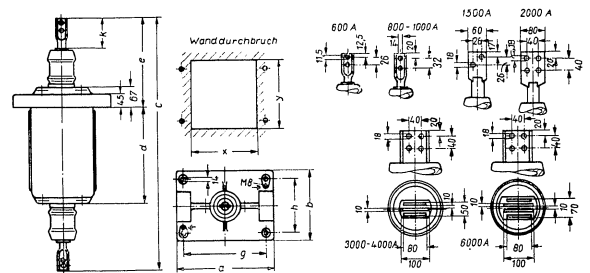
Maßzeichnung für Stabstromwandler Form ARP
